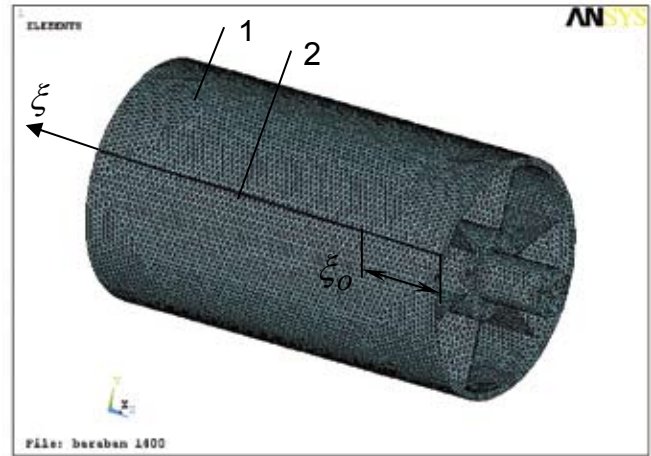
Модель барабана ленточного конвейера: 1 – обечайка; 2 – анализируемый сварной шов
